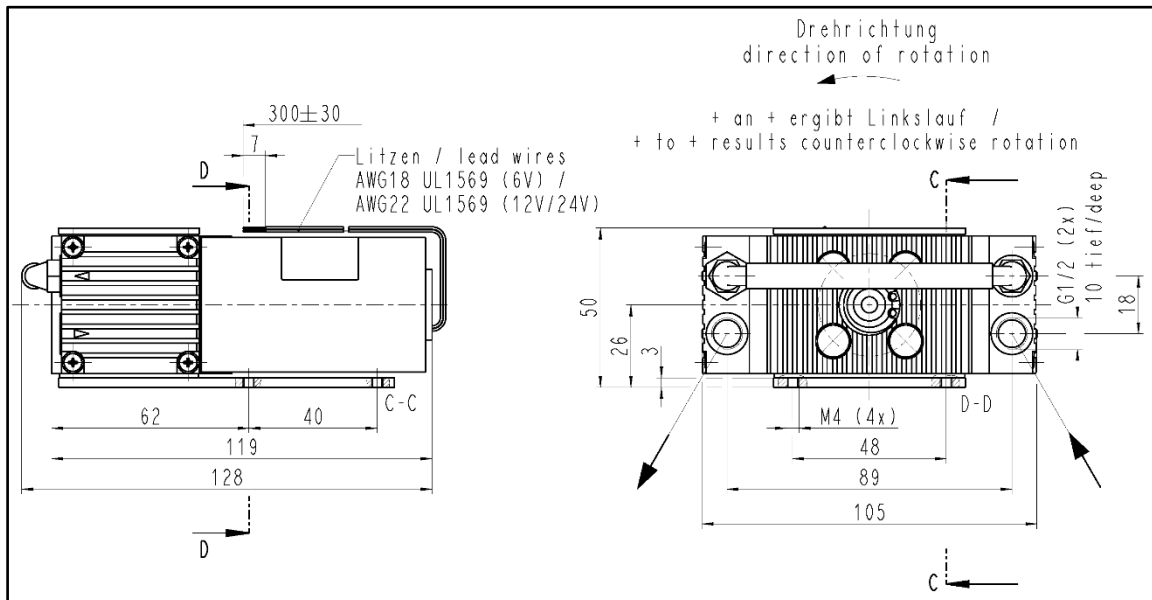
Befestigungsmaße Pumpenreihe N85.3K_DC
